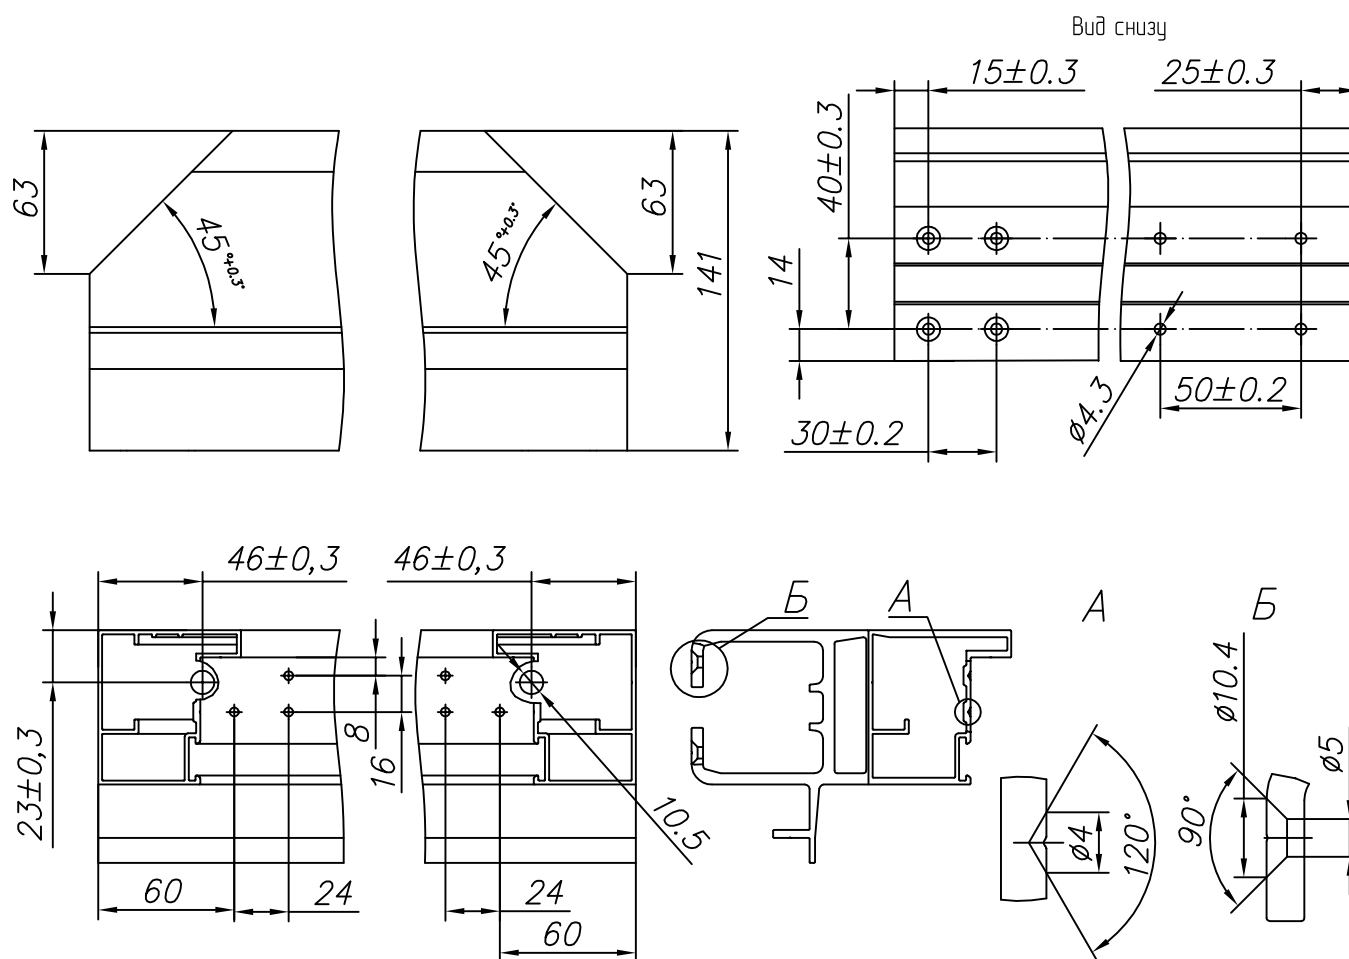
Изготовление шины для пассивной (опорной) створки (открывание влево)
